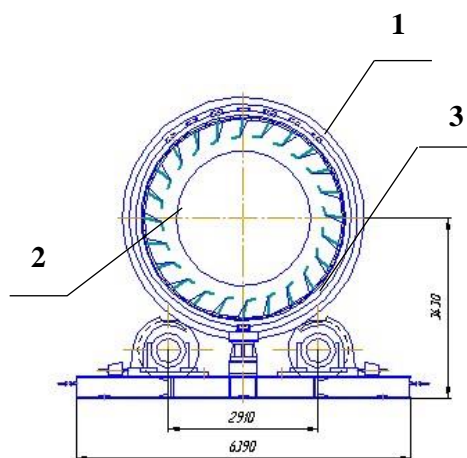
Барабанный гранулятор для формования топливных гранул: 1 - полый цилиндрический барабан; 2 - лопатки для загрузки смеси и выгрузки топливных гранул; 3 - бандажные опоры.
